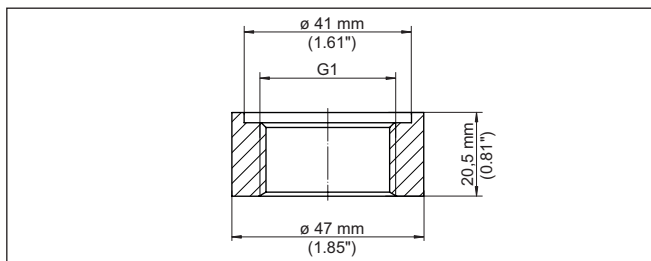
Medidas racor soldado G1 (ISO 228)
